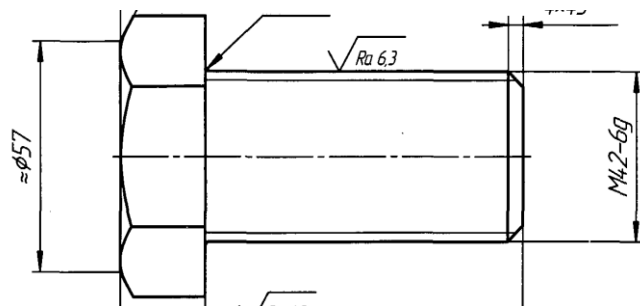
Эскиз детали «Болт», материал – сталь 35ХМ.
